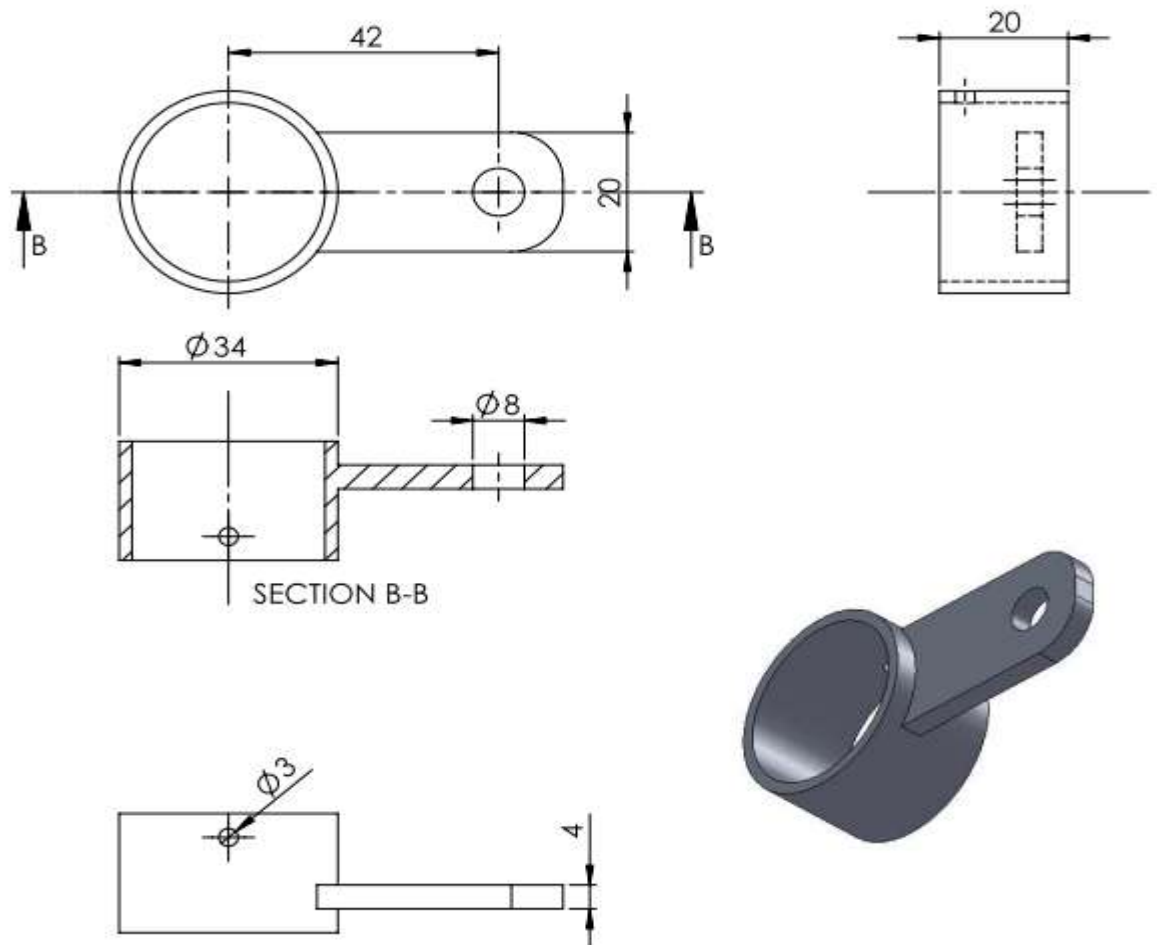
Dessin de définition des anneaux des mors mobile et fixe
